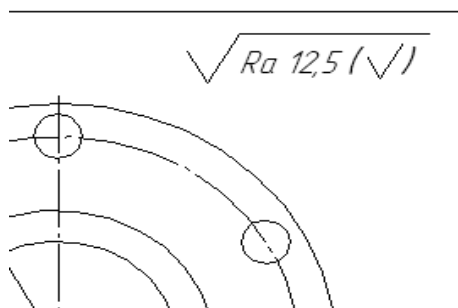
Обозначение неуказанной шероховатости поверхности
